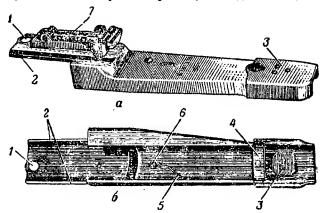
Кронштейл: 1 — выступы для зацепа коробки; 2 — флажок; 3 — ось флажка; 4 — пластинчатая пружина
